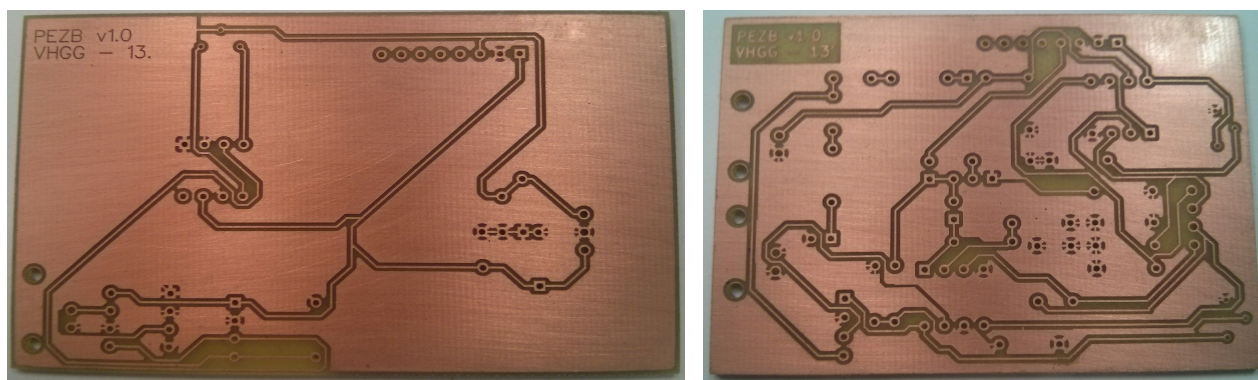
Primeras placas, versión inicial. Módulo base a la izquierda y módulo apilable a la derecha
